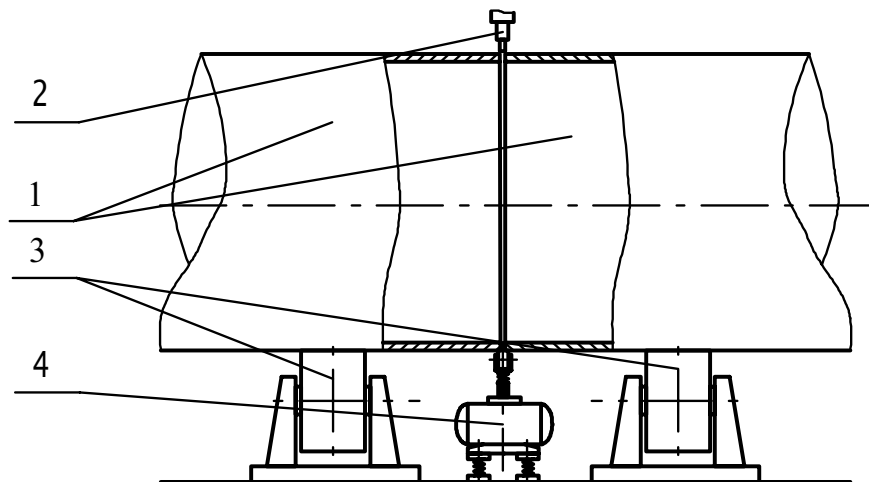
Схема сопутствующей виброобработки при сварке соединений крупногабаритных деталей:
